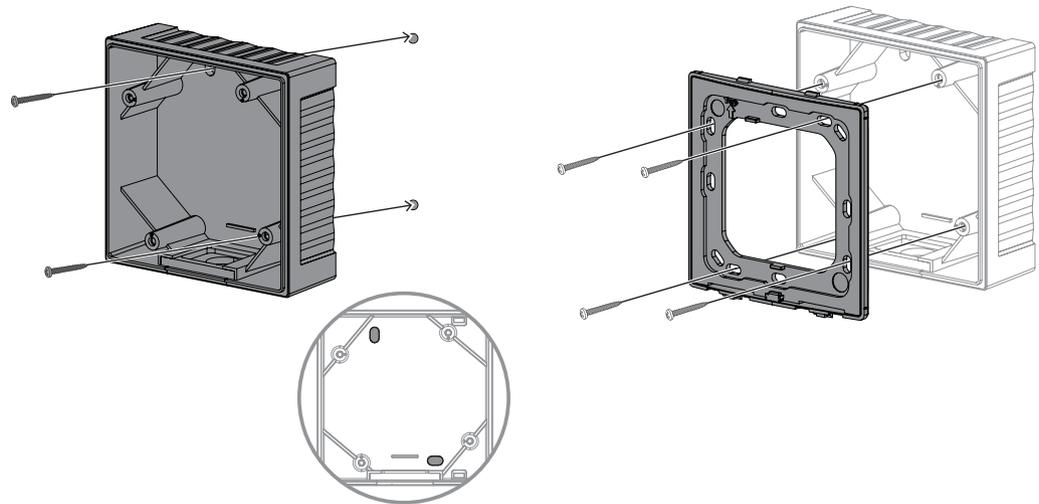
Montagem do suporte do leitor na instalação na superfície
